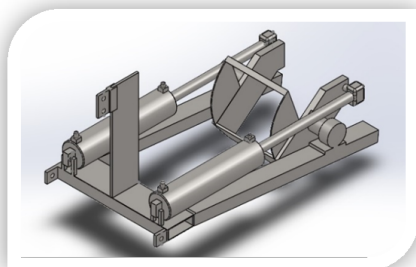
Конструкция выкопчной машины: 1 – рама с несущими брусками; 2 – навесное устройство; 3 – вертикальные стойки; 4 – подкапывающий рабочий орган; 5 – полуковш; 6 – гидроцилиндр; 7 – шарниры; 8 – опоры; 9 – ограничитель
